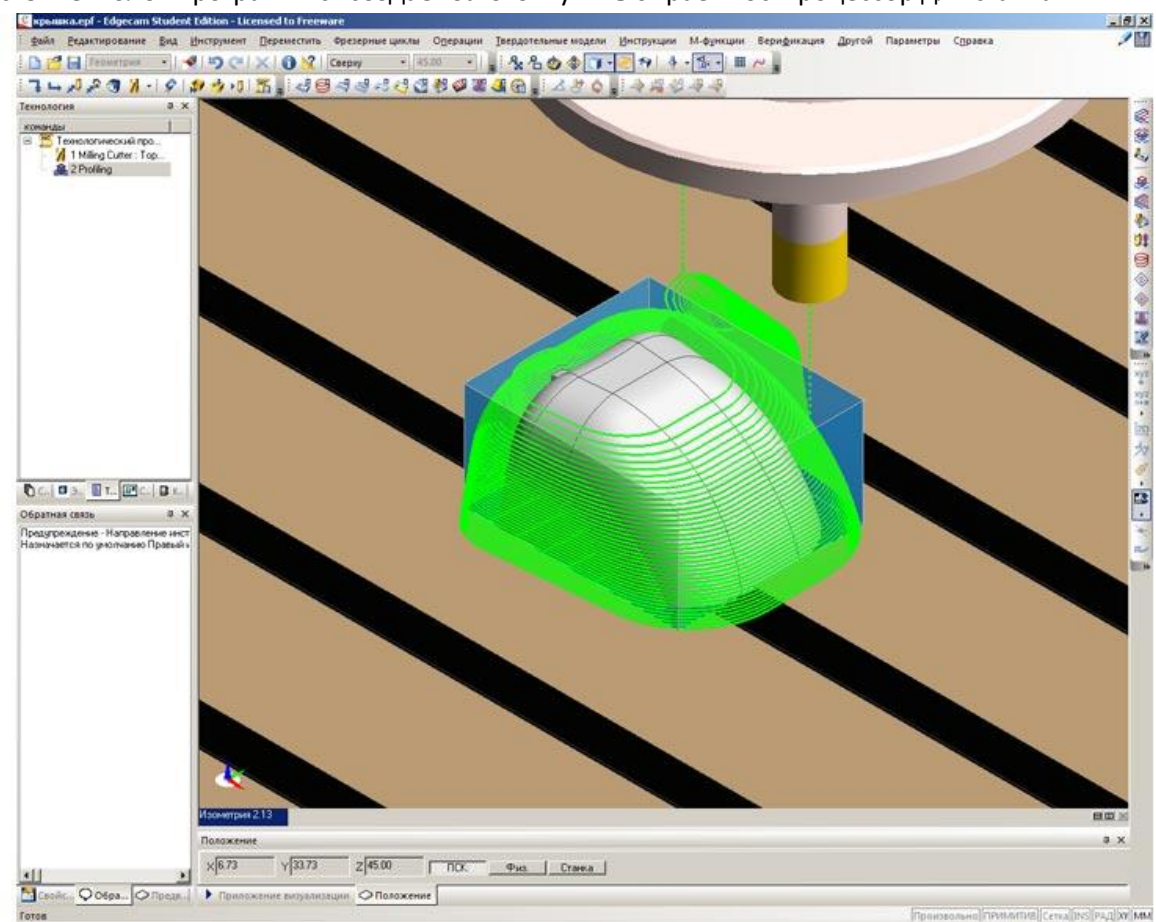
Выбирается черновой инструмент и назначается предварительная обработка заготовки
